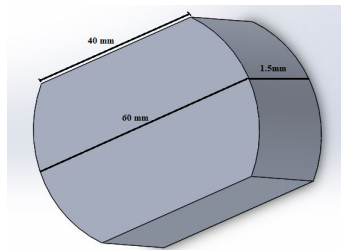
Dimensiones del diseño de la base chip LED en SOLIDWORKS®.
